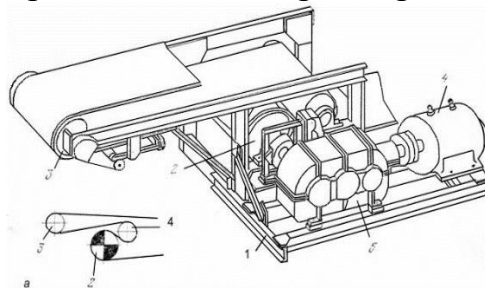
Конструкція приводу стрічкового конвеєра
